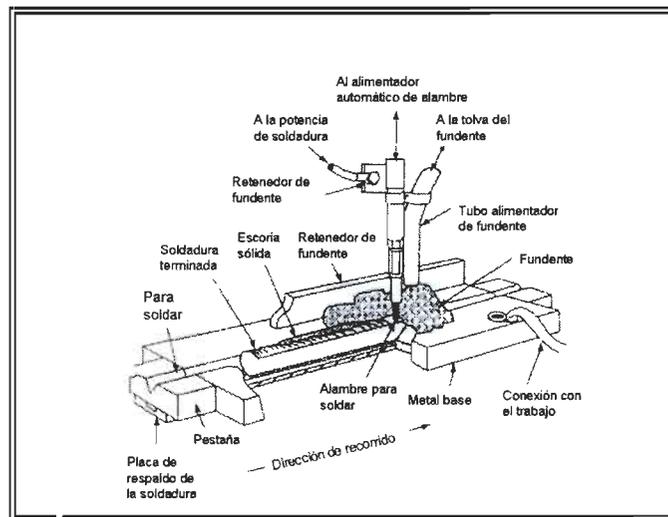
Diagrama proceso de soldadura SAW
